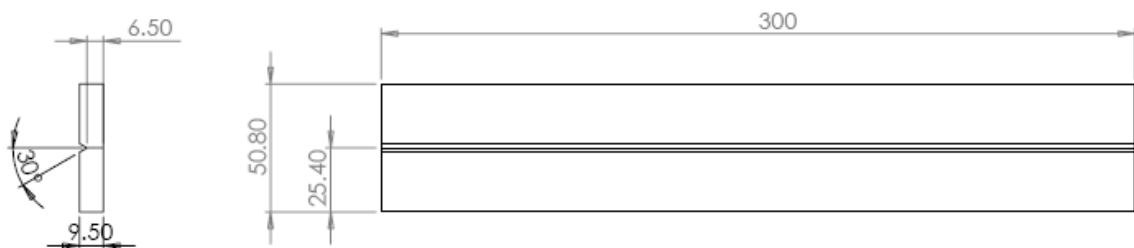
Dimensões e geometria da junta utilizada para soldagens com transferência gótica
